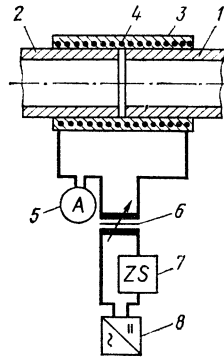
Сварка фитингов и втулок нагретой проволокой: 1, 2 — свариваемые детали (трубы); 3 — свариваемая втулка или фитинг с нагревающей проволокой; 4 — нагретая проволока (нихром или медь); 5 — измеритель тока; 6 — регулировочный трансформатор; 7 — реле времени; 8 — источник питания
